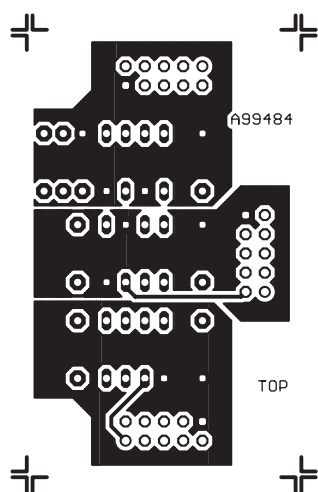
Schéma zapojení adapteru pro speciální obvody A99484
